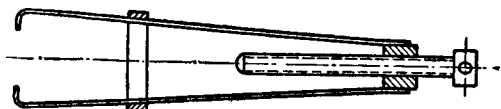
Приспособление для снятия втулки двигателя напряжения
